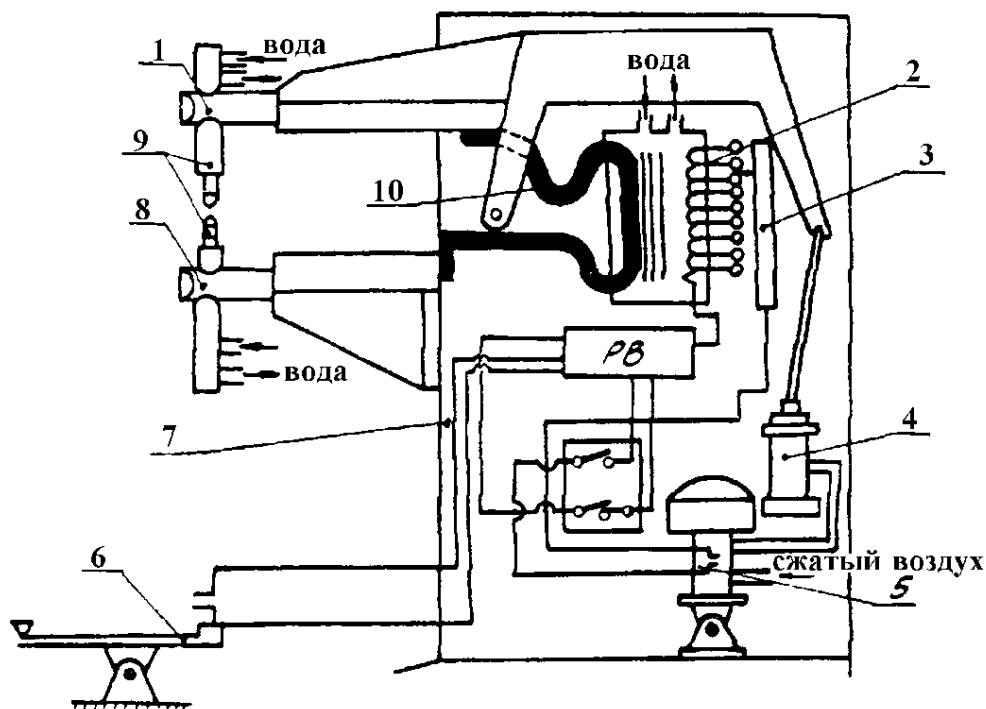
Схема машины для точечной сварки МТ-601
